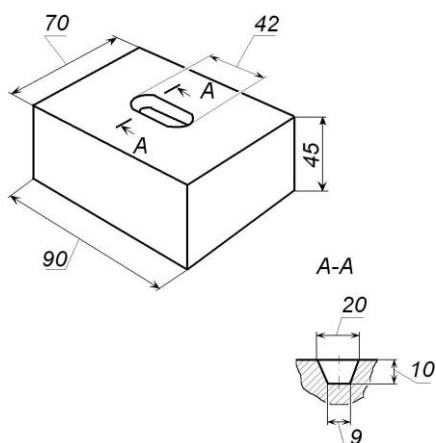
Образец для имитации ремонтной сварки с выходом дуги в основной металл корпуса реактора
